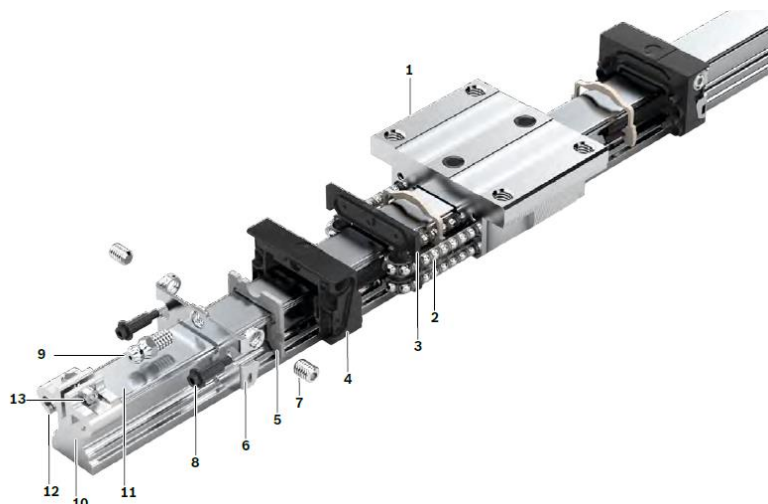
Конструктивные элементы профильной рельсовой направляющей:
